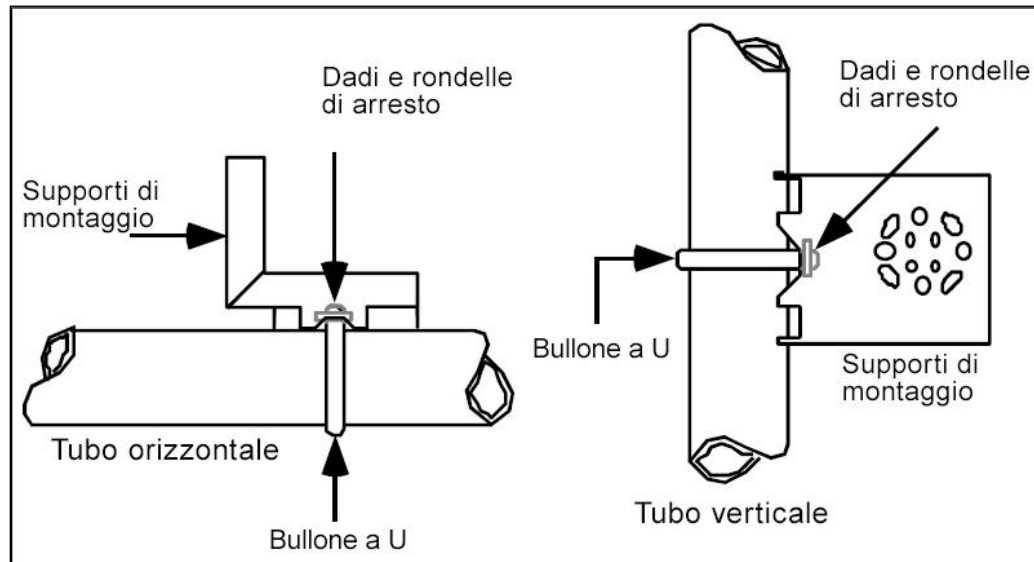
Supporto di montaggio angolare fissato a un tubo orizzontale o verticale
